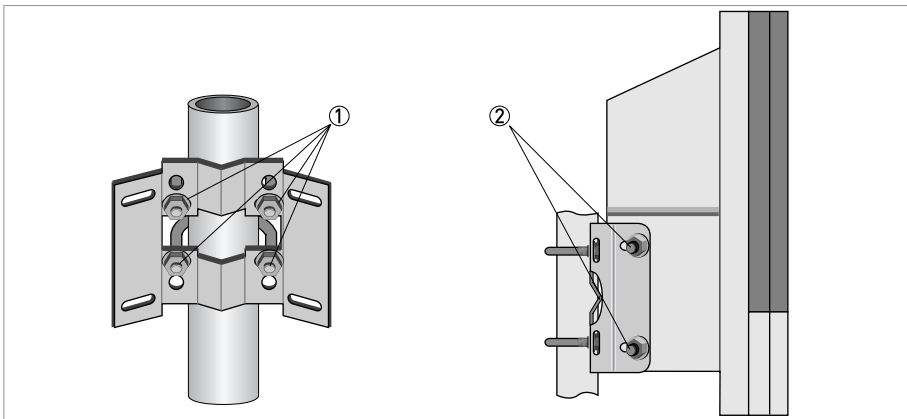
Крепление преобразователя сигналов для настенного монтажа на стойке
